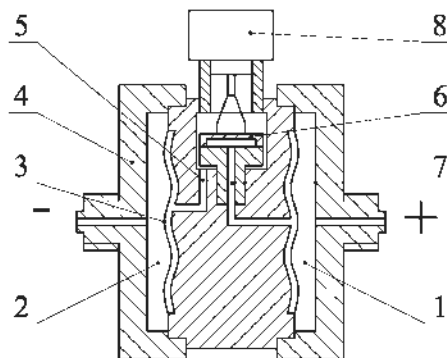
Схема первичного измерительного преобразователя приборов РПД-Д: 1 – плюсовая камера, 2 – минусовая камера, 3 – металлическая мембрана, 4 – корпус, 5 – канал минусового давления, 6 – чувствительный элемент, 7 – канал плюсового давления, 8 – блок усиления и преобразования выходного сигнала измерительного преобразователя в нормированный выходной сигнал постоянного тока или напряжения.
